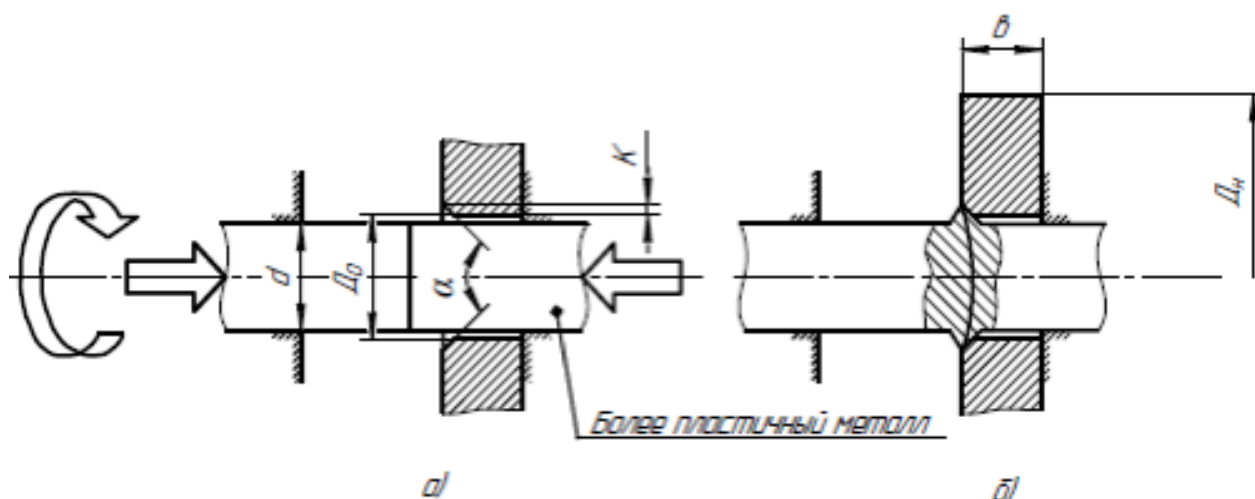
Схема сварки трением разнородных металлов с применением оправки
